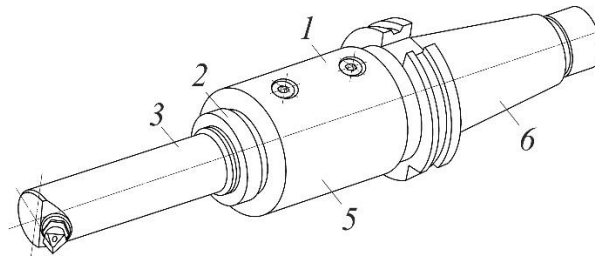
Приспособление для растачивания: 1 - передняя часть базисного агрегата; 2 - регулировочная гайка; 3 – сменная наладка; 6 – хвостовик базисного агрегата
